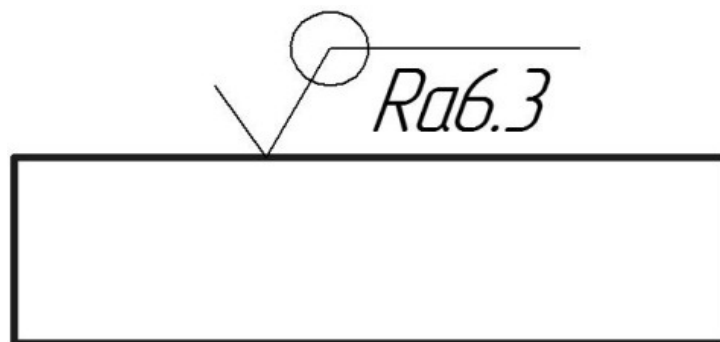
Обозначение одинаковой шероховатости поверхностей, образующих замкнутый контур
